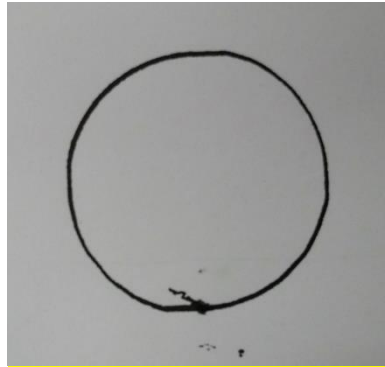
Primera prueba. Un círculo realizado con Machinekit
